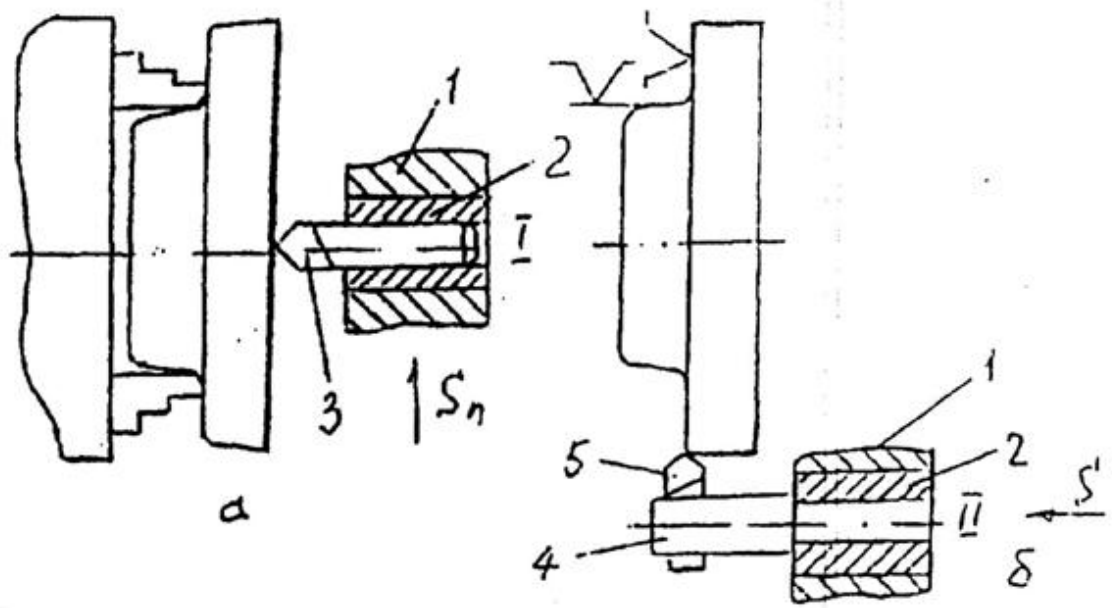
Схема обработки на 035-й токарно-револьверной операции: а – подрезка торца на I позиции; б – точение наружной цилиндрической поверхности на II позиции револьверной головки. 1 – револьверная головка; 2 – втулка; 3 – токарный подрезной резец; 4 – державка для токарного проходного резца
